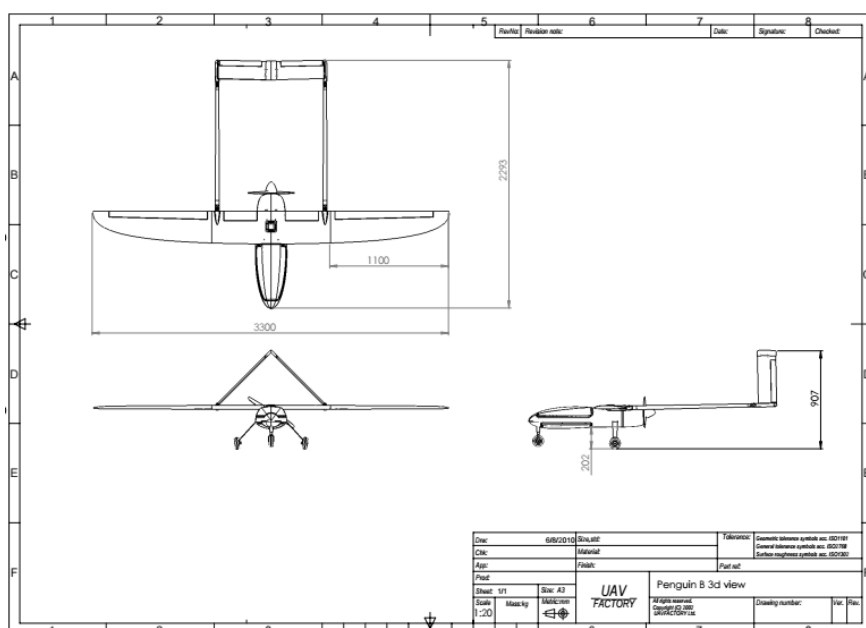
Planta, alzado y perfil del Penguin B. (Factory s.f.)
